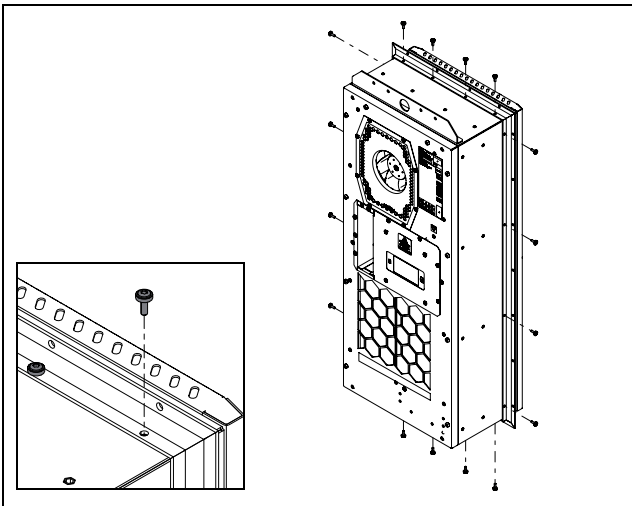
Fixação do quadro de montagem no condicionador de ar
